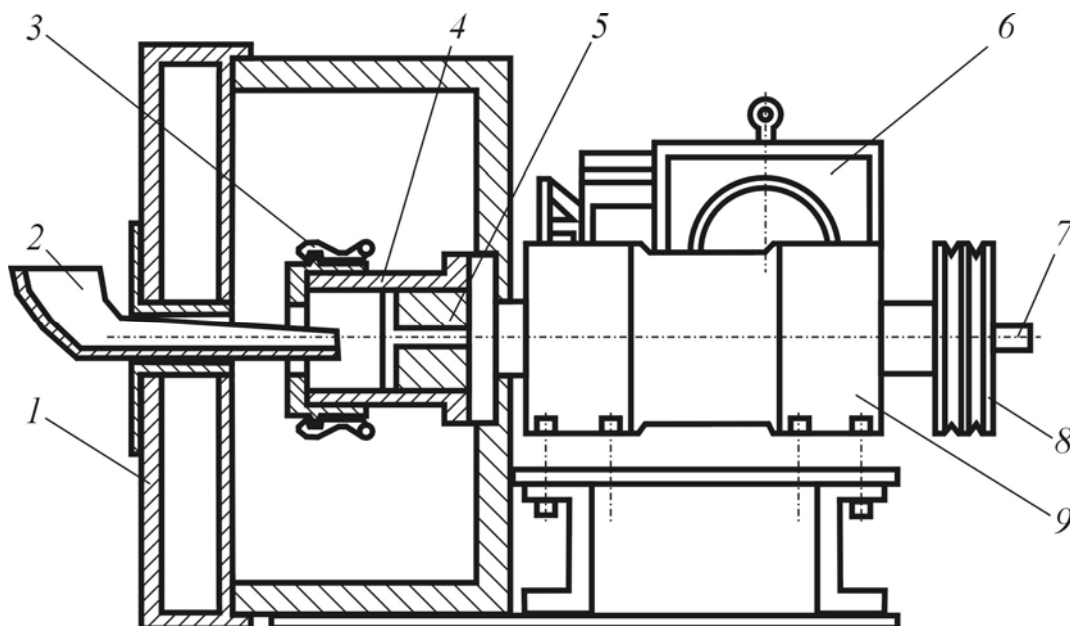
Відцентрова машина: 1 – дверцята; 2 – жолоб; 3 – відцентрові затиски; 4 – виливниця; 5 – змінна вставка; 6 – варіатор швидкості; 7 – шток виштовхувача; 8 – шків; 9 – корпус підшипника
